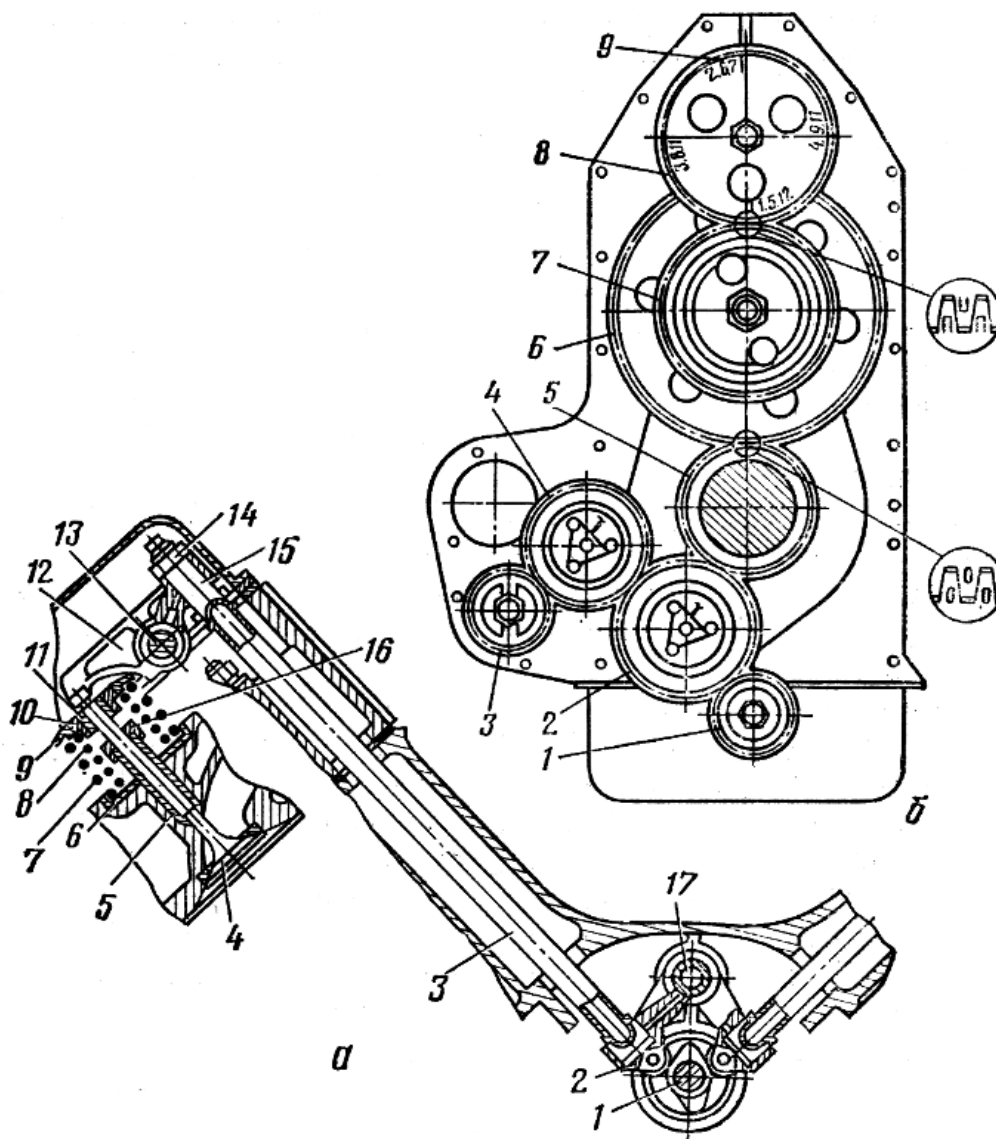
Газораспределительный механизм двигателя ЯМЗ-240Б:
